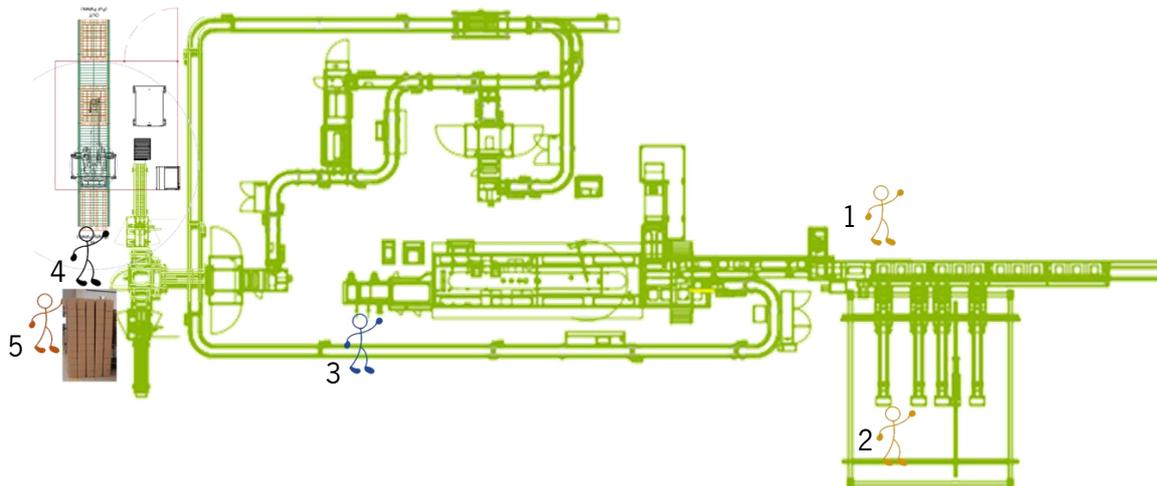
Layout* da Bolero com a disposição dos trabalhadores na produção da revista A
